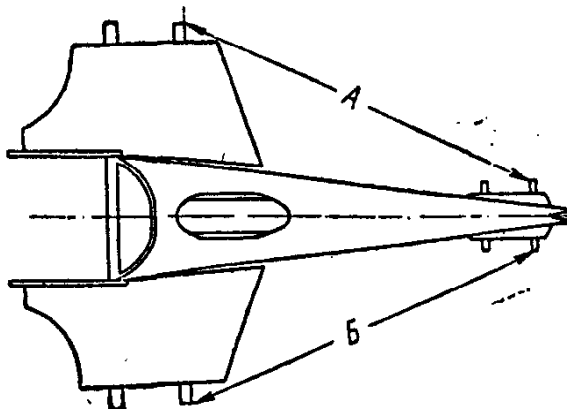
Стапель для стыковки фюзеляжа с центропланом.
